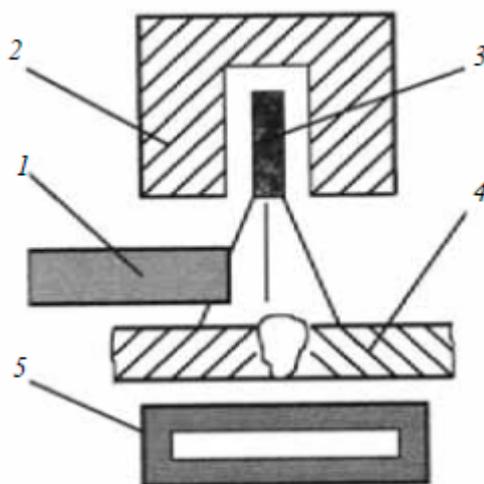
Схема просвечивания гамма-лучами: 1 – затвор; 2 – свинцовая капсула; 3 – капсула с веществом; 4 – сварное соединение; 5 – кассета с пленкой
